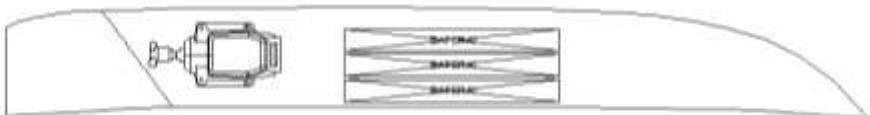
Deck Tunnel* USV PLAT-N
